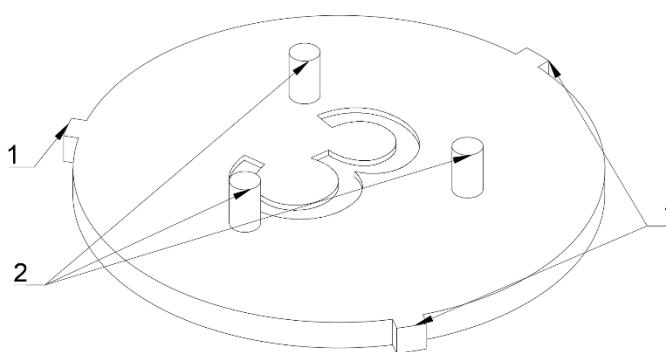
Схематическое изображение пластины, формирующей кольцевой зазор шириной 3 мм. 1 – краевые упоры, формирующие зазор, 2 – торцевые упоры.
